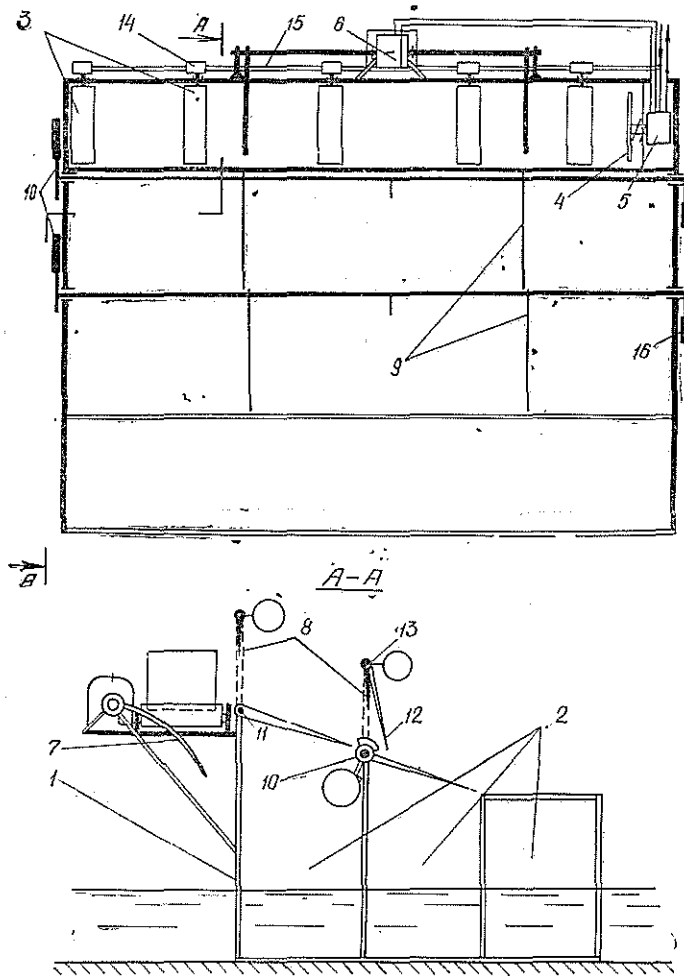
Схема устройства для автоматической сортировки бревен по размерам.
